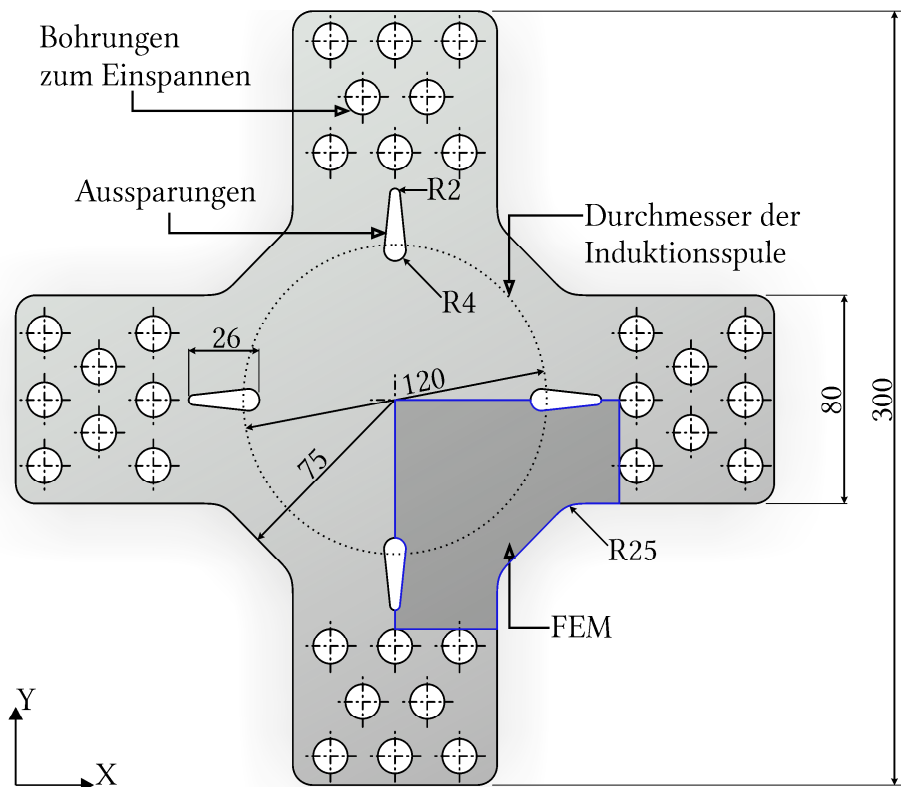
Abmessungen der neuentwickelten Kreuzzugproben; die Bohrungen sind zum Durchstecken der Befestigungsschrauben, damit die Probe zwischen zwei Werkzeugen flächig eingespannt wird (Kerbwirkung vermeiden)
